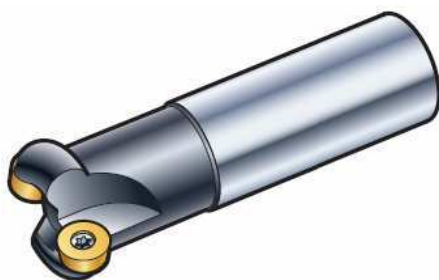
Frézování drážek planetovým způsobem<sup>3</sup>
